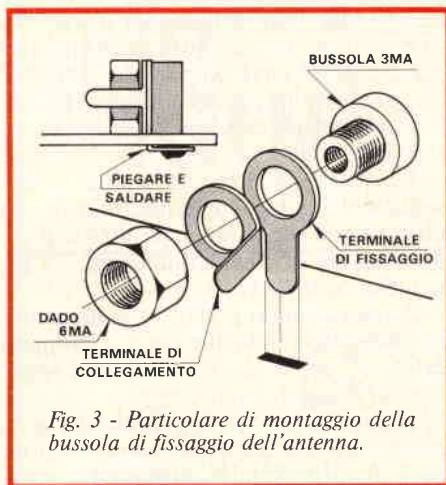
Particolare di montaggio della bussola di fissaggio dell'antenna.
